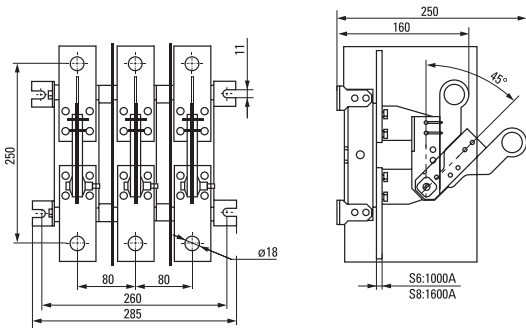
Габаритные и установочные размеры разъединителя типа PE19-41/43 с рычагом для полюсного оперирования штангой
